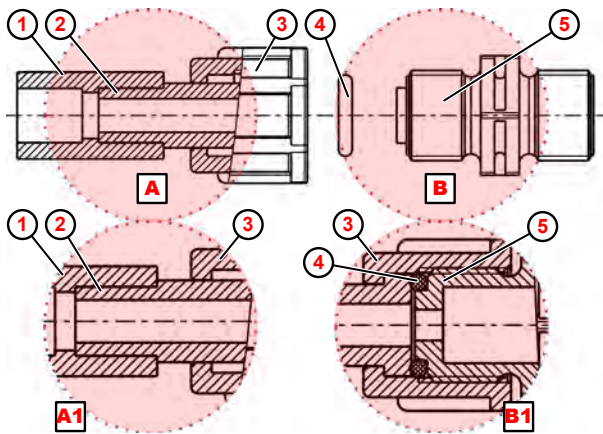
Rohranschluss mit Aufschweißverbindung
